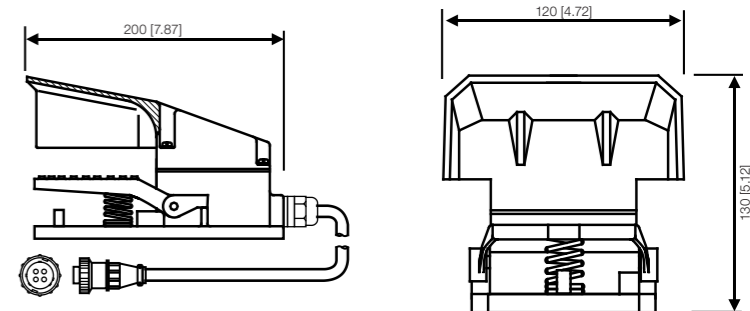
Footswitch - Dimensiones in millimeters [inches]
